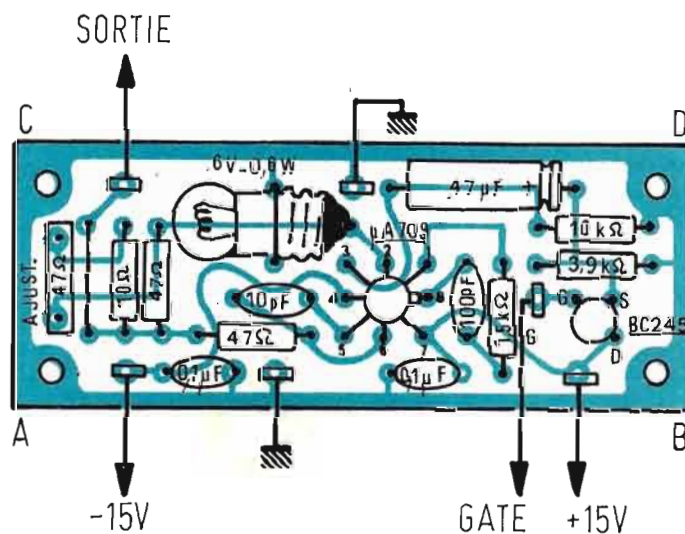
Carte imprimée d'oscillateur expérimental.
